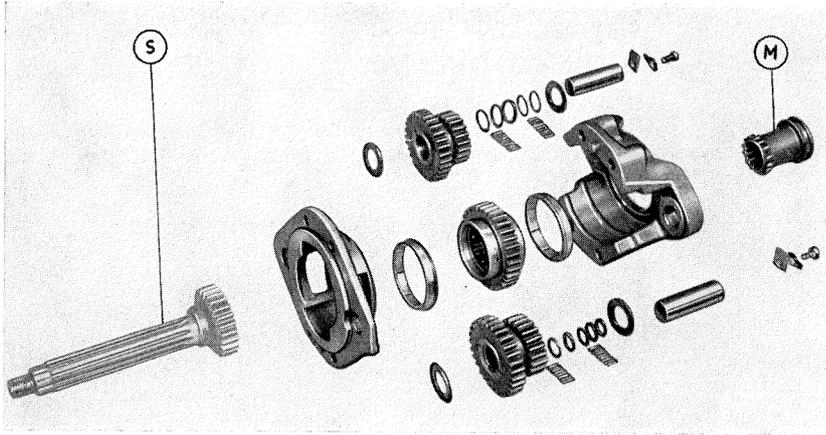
Pièces du réducteur de la boîte de vitesses.
